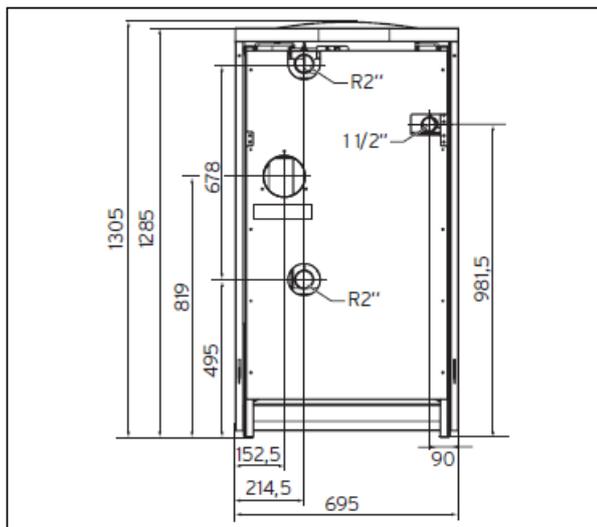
Присоединительные размеры патрубков (в мм)
